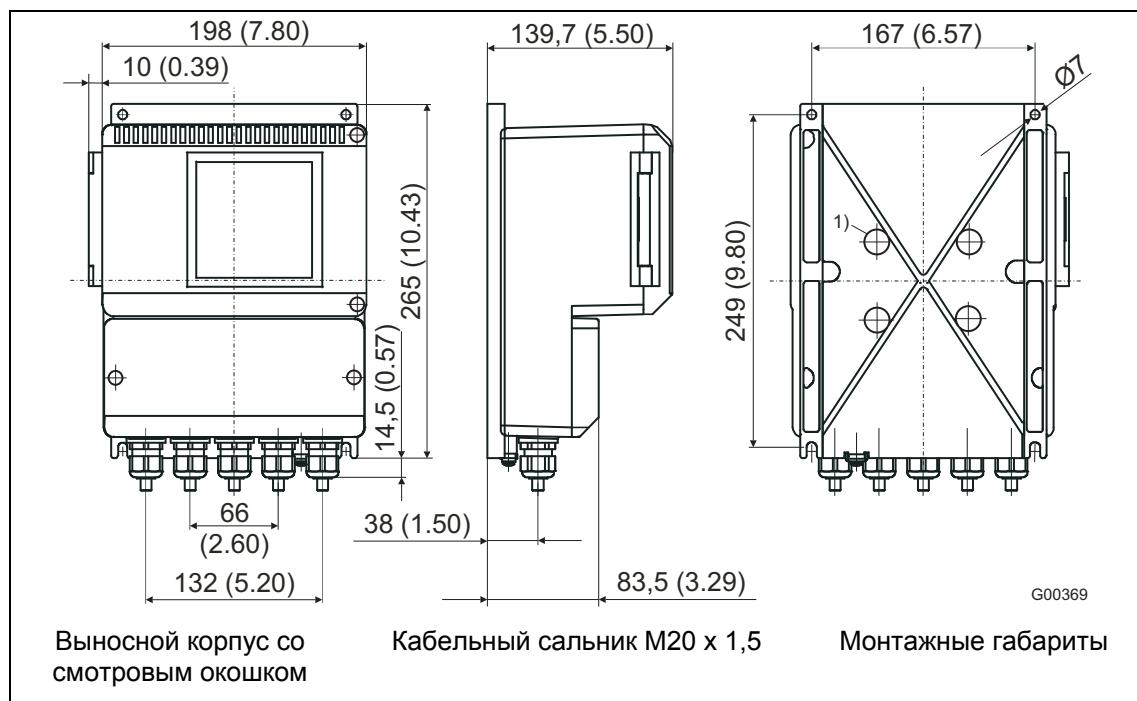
габариты корпуса измерительного преобразователя ME21 / 22 / 23 / 24 / 25
